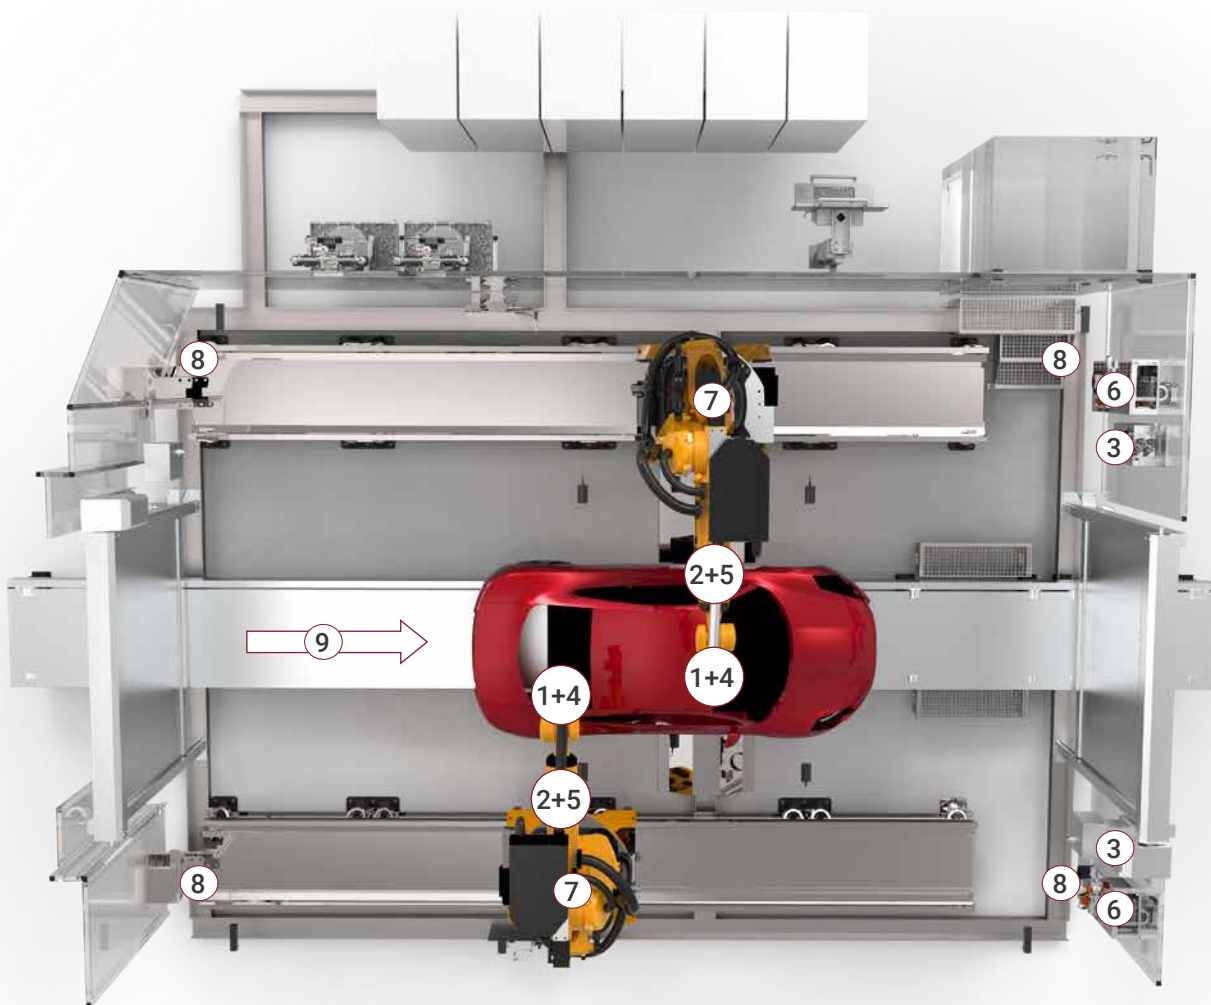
Aufbau einer Finish-Zelle bei einem OEM (paralleles Layout)
